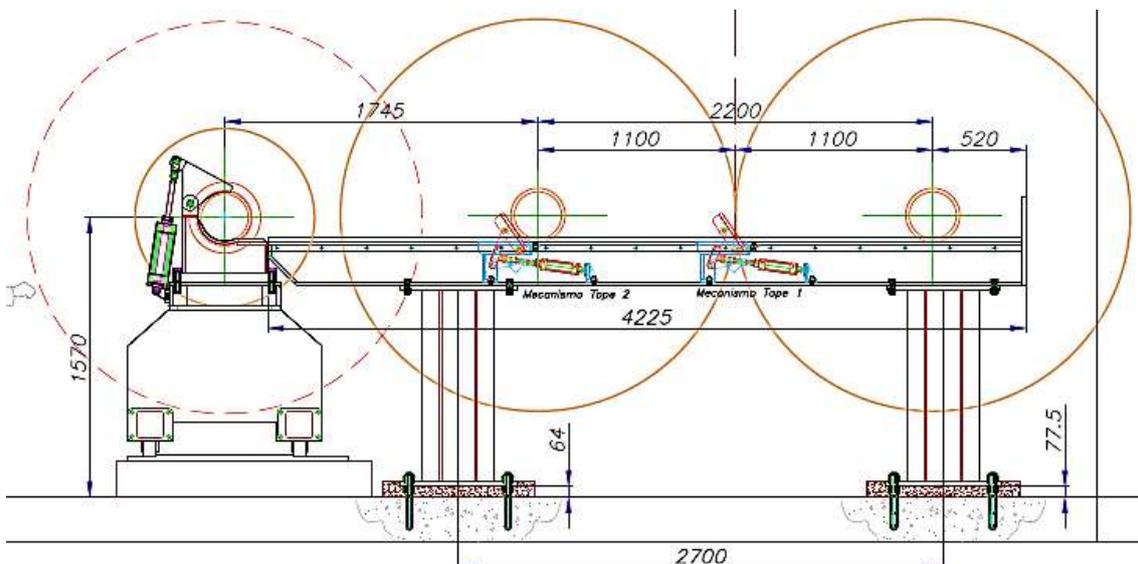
Bobinas sobre Stand Reel Fuente: (Autor)
